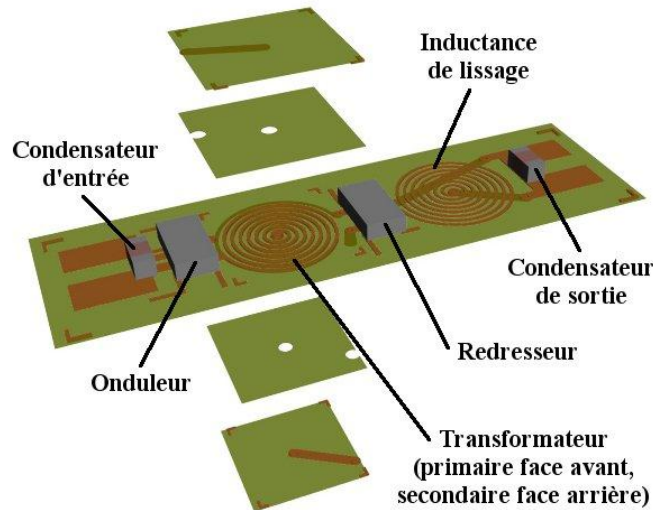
Vue en 3D du micro-convertisseur avec les bobinages intégrés au PCB sur Kapton
